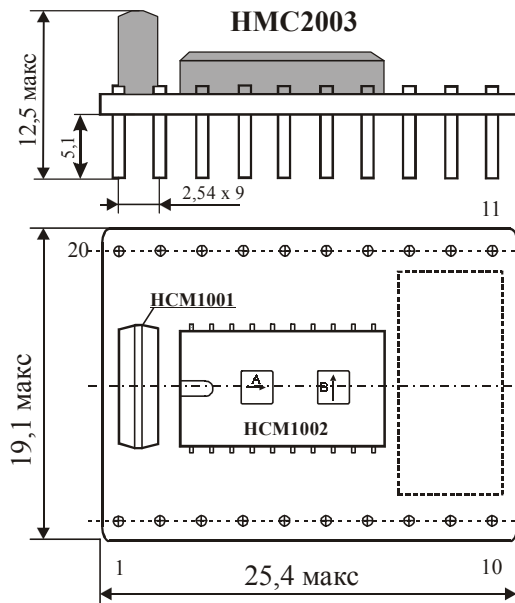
Внешний вид и габаритные размеры датчиков типа HMC 2003
